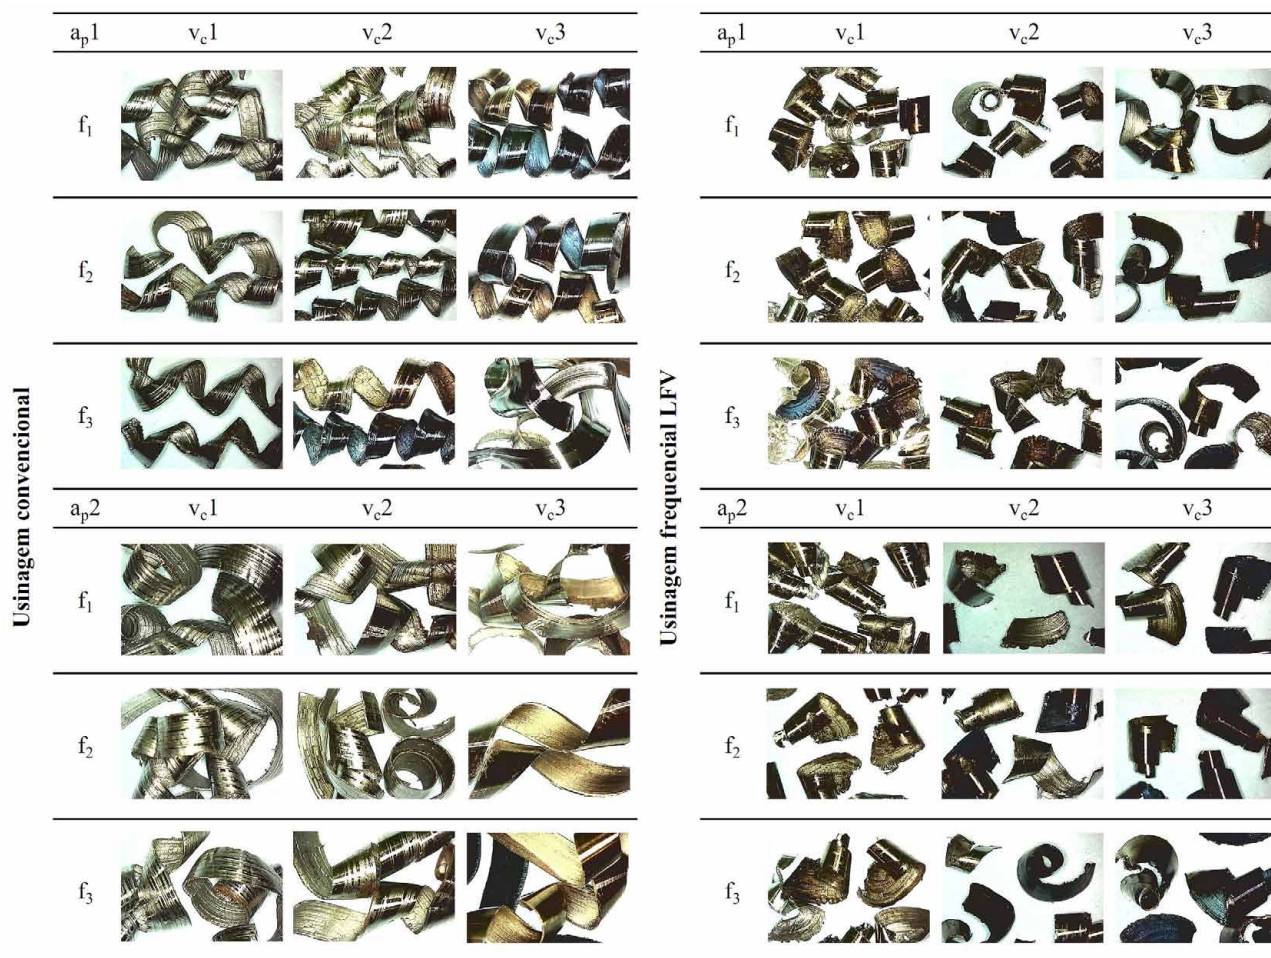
Geometria dos cavacos para usinagem convencional e usinagem LFV.
